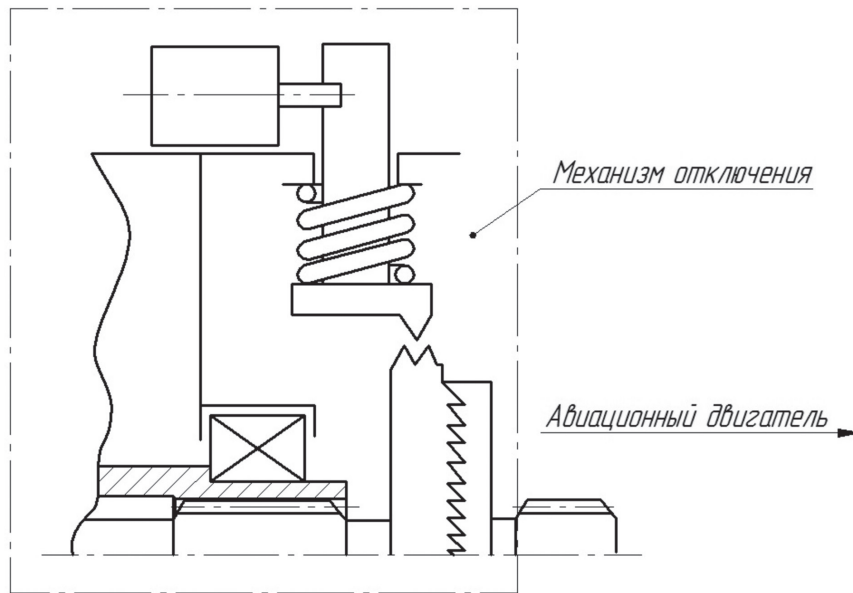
Конструктивная схема механизма отключения в стыковочной части корпуса генератора
